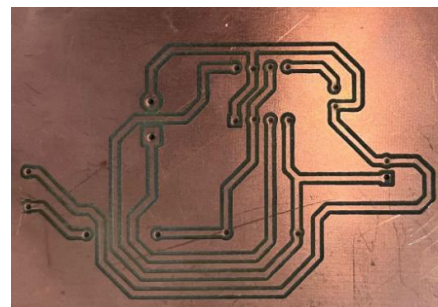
Resultado final de PCB fabricada con Máquina CNC
